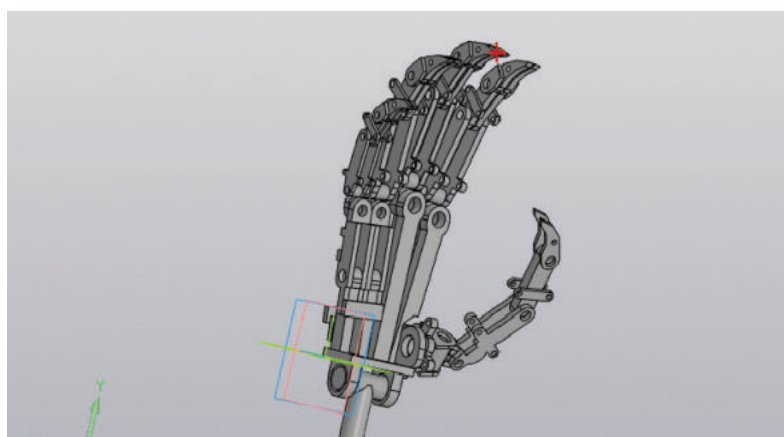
3D-модель конструкторской разработки (вид сбоку)
